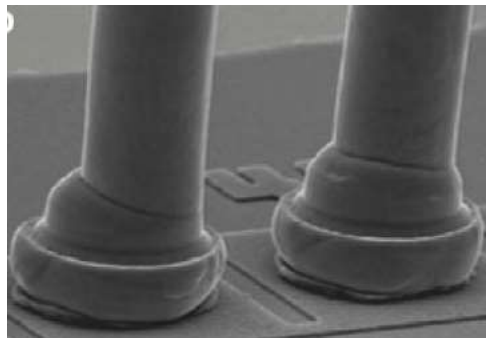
Bola soldada de cobre de 43 µm de diámetro. [3]
